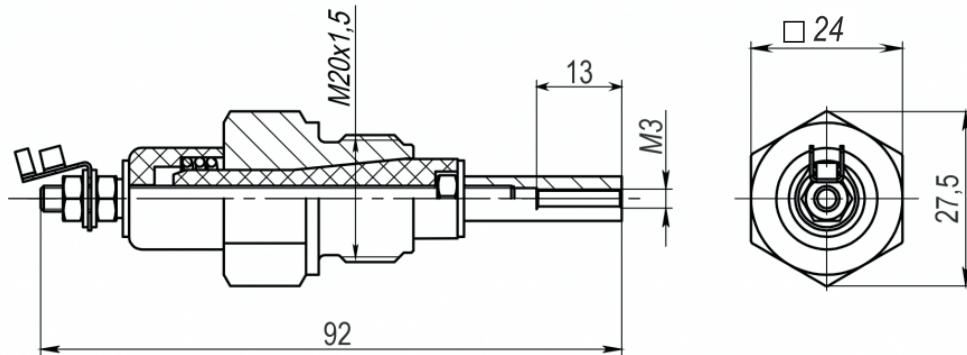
габаритные и установочные размеры датчика КДУ-1Э
